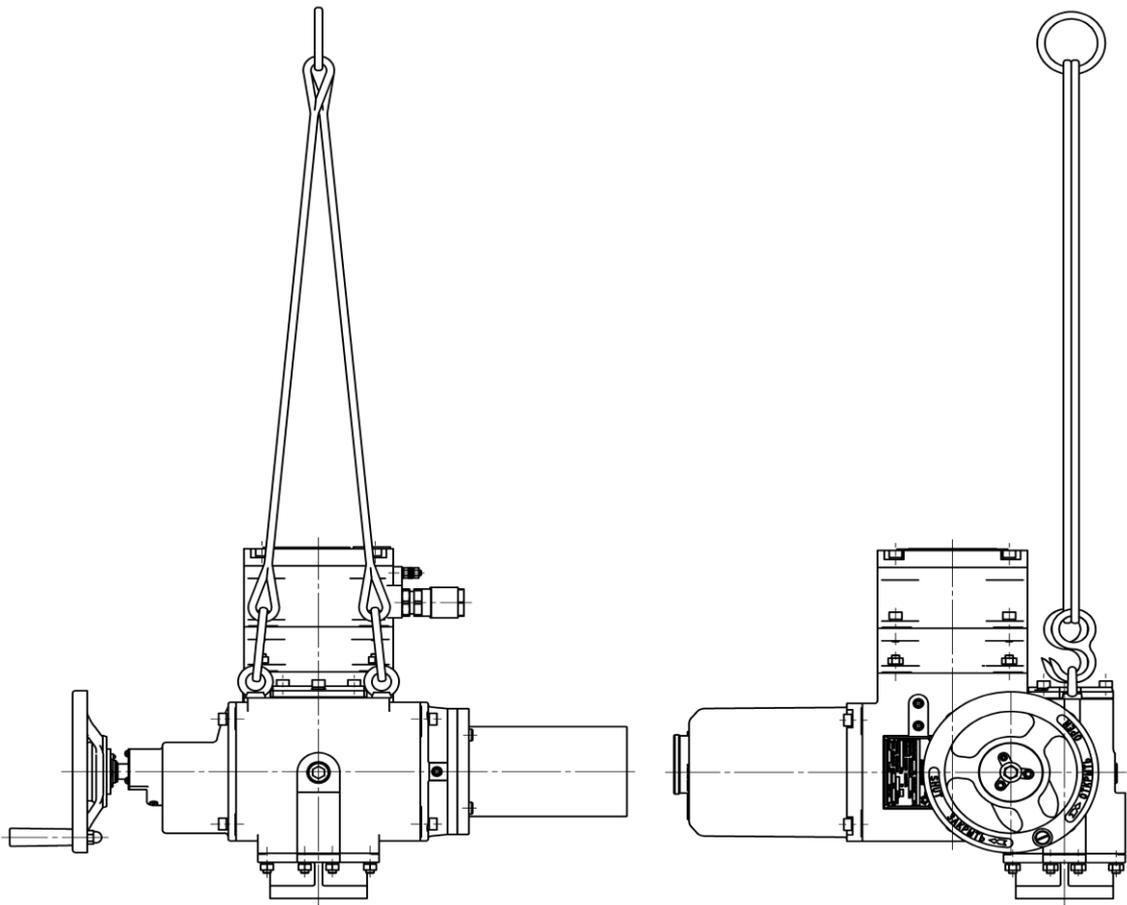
а – Схема строповки привода конструктивной схемы 40
